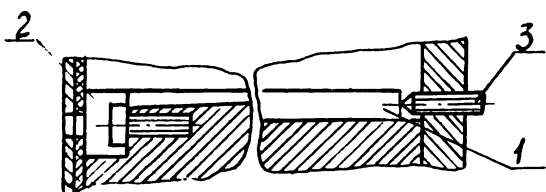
Регулирование зазора в направляющих резцовых салазках суппорта
